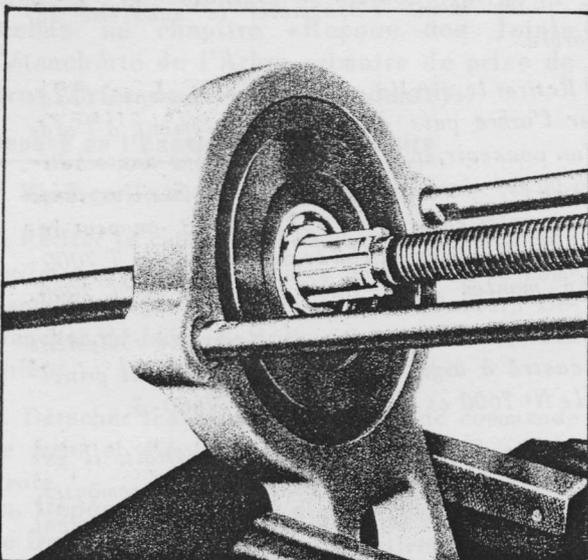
= Depose du Roulement arriere d'Arbre de renvoi de Prise de force
